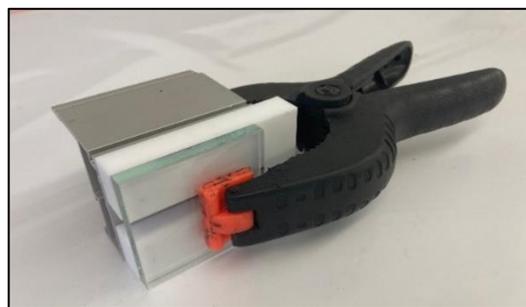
assemblage : écarteur en téflon blanc (en U) et supports en verre et aluminium
